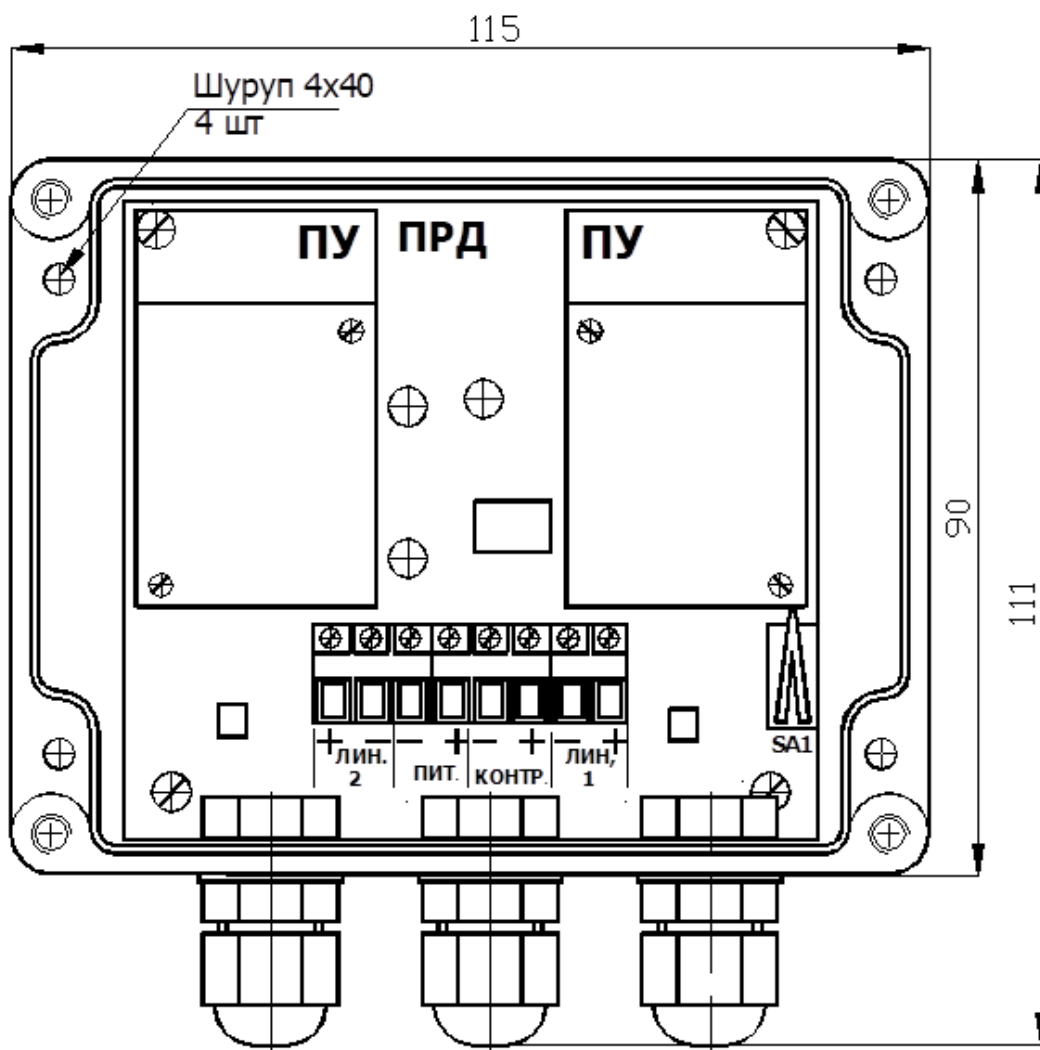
Общий вид модуля ПРД в корпусе со снятой крышкой и с установленными модулями ПУ
